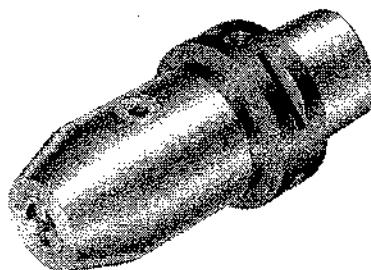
Сверлильный патрон C6-391.31-13 092
